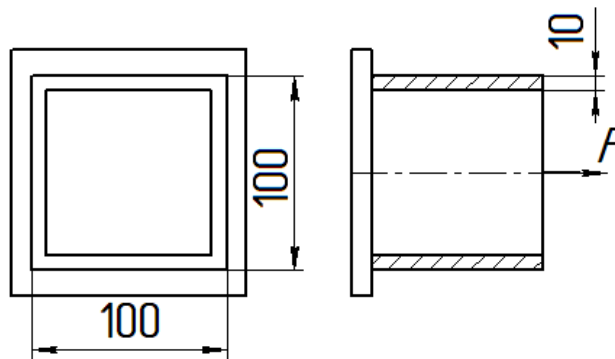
Расчетная схема таврового сварного соединения
